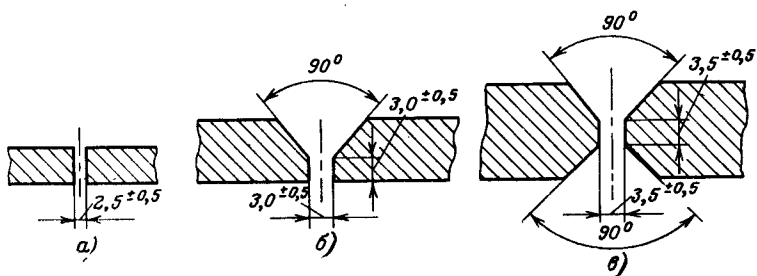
Механическая обработка заготовок короткозамыкающих колец под сварку.
